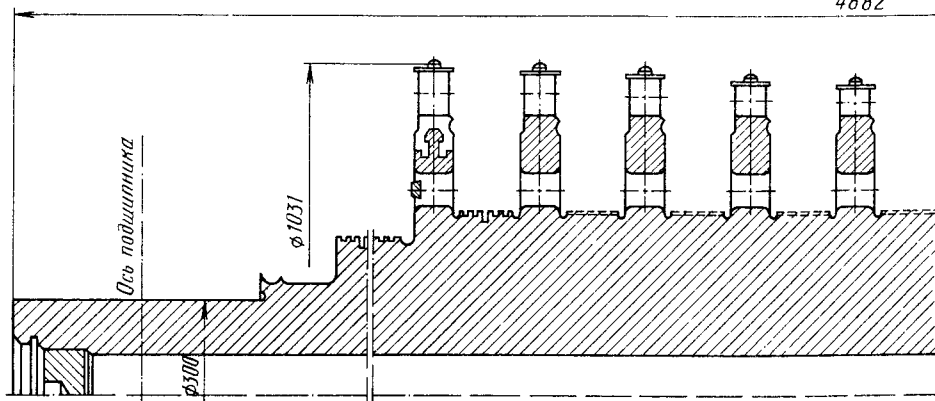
Цельнокованный ротор для ЦВД турбины ХТЗ
